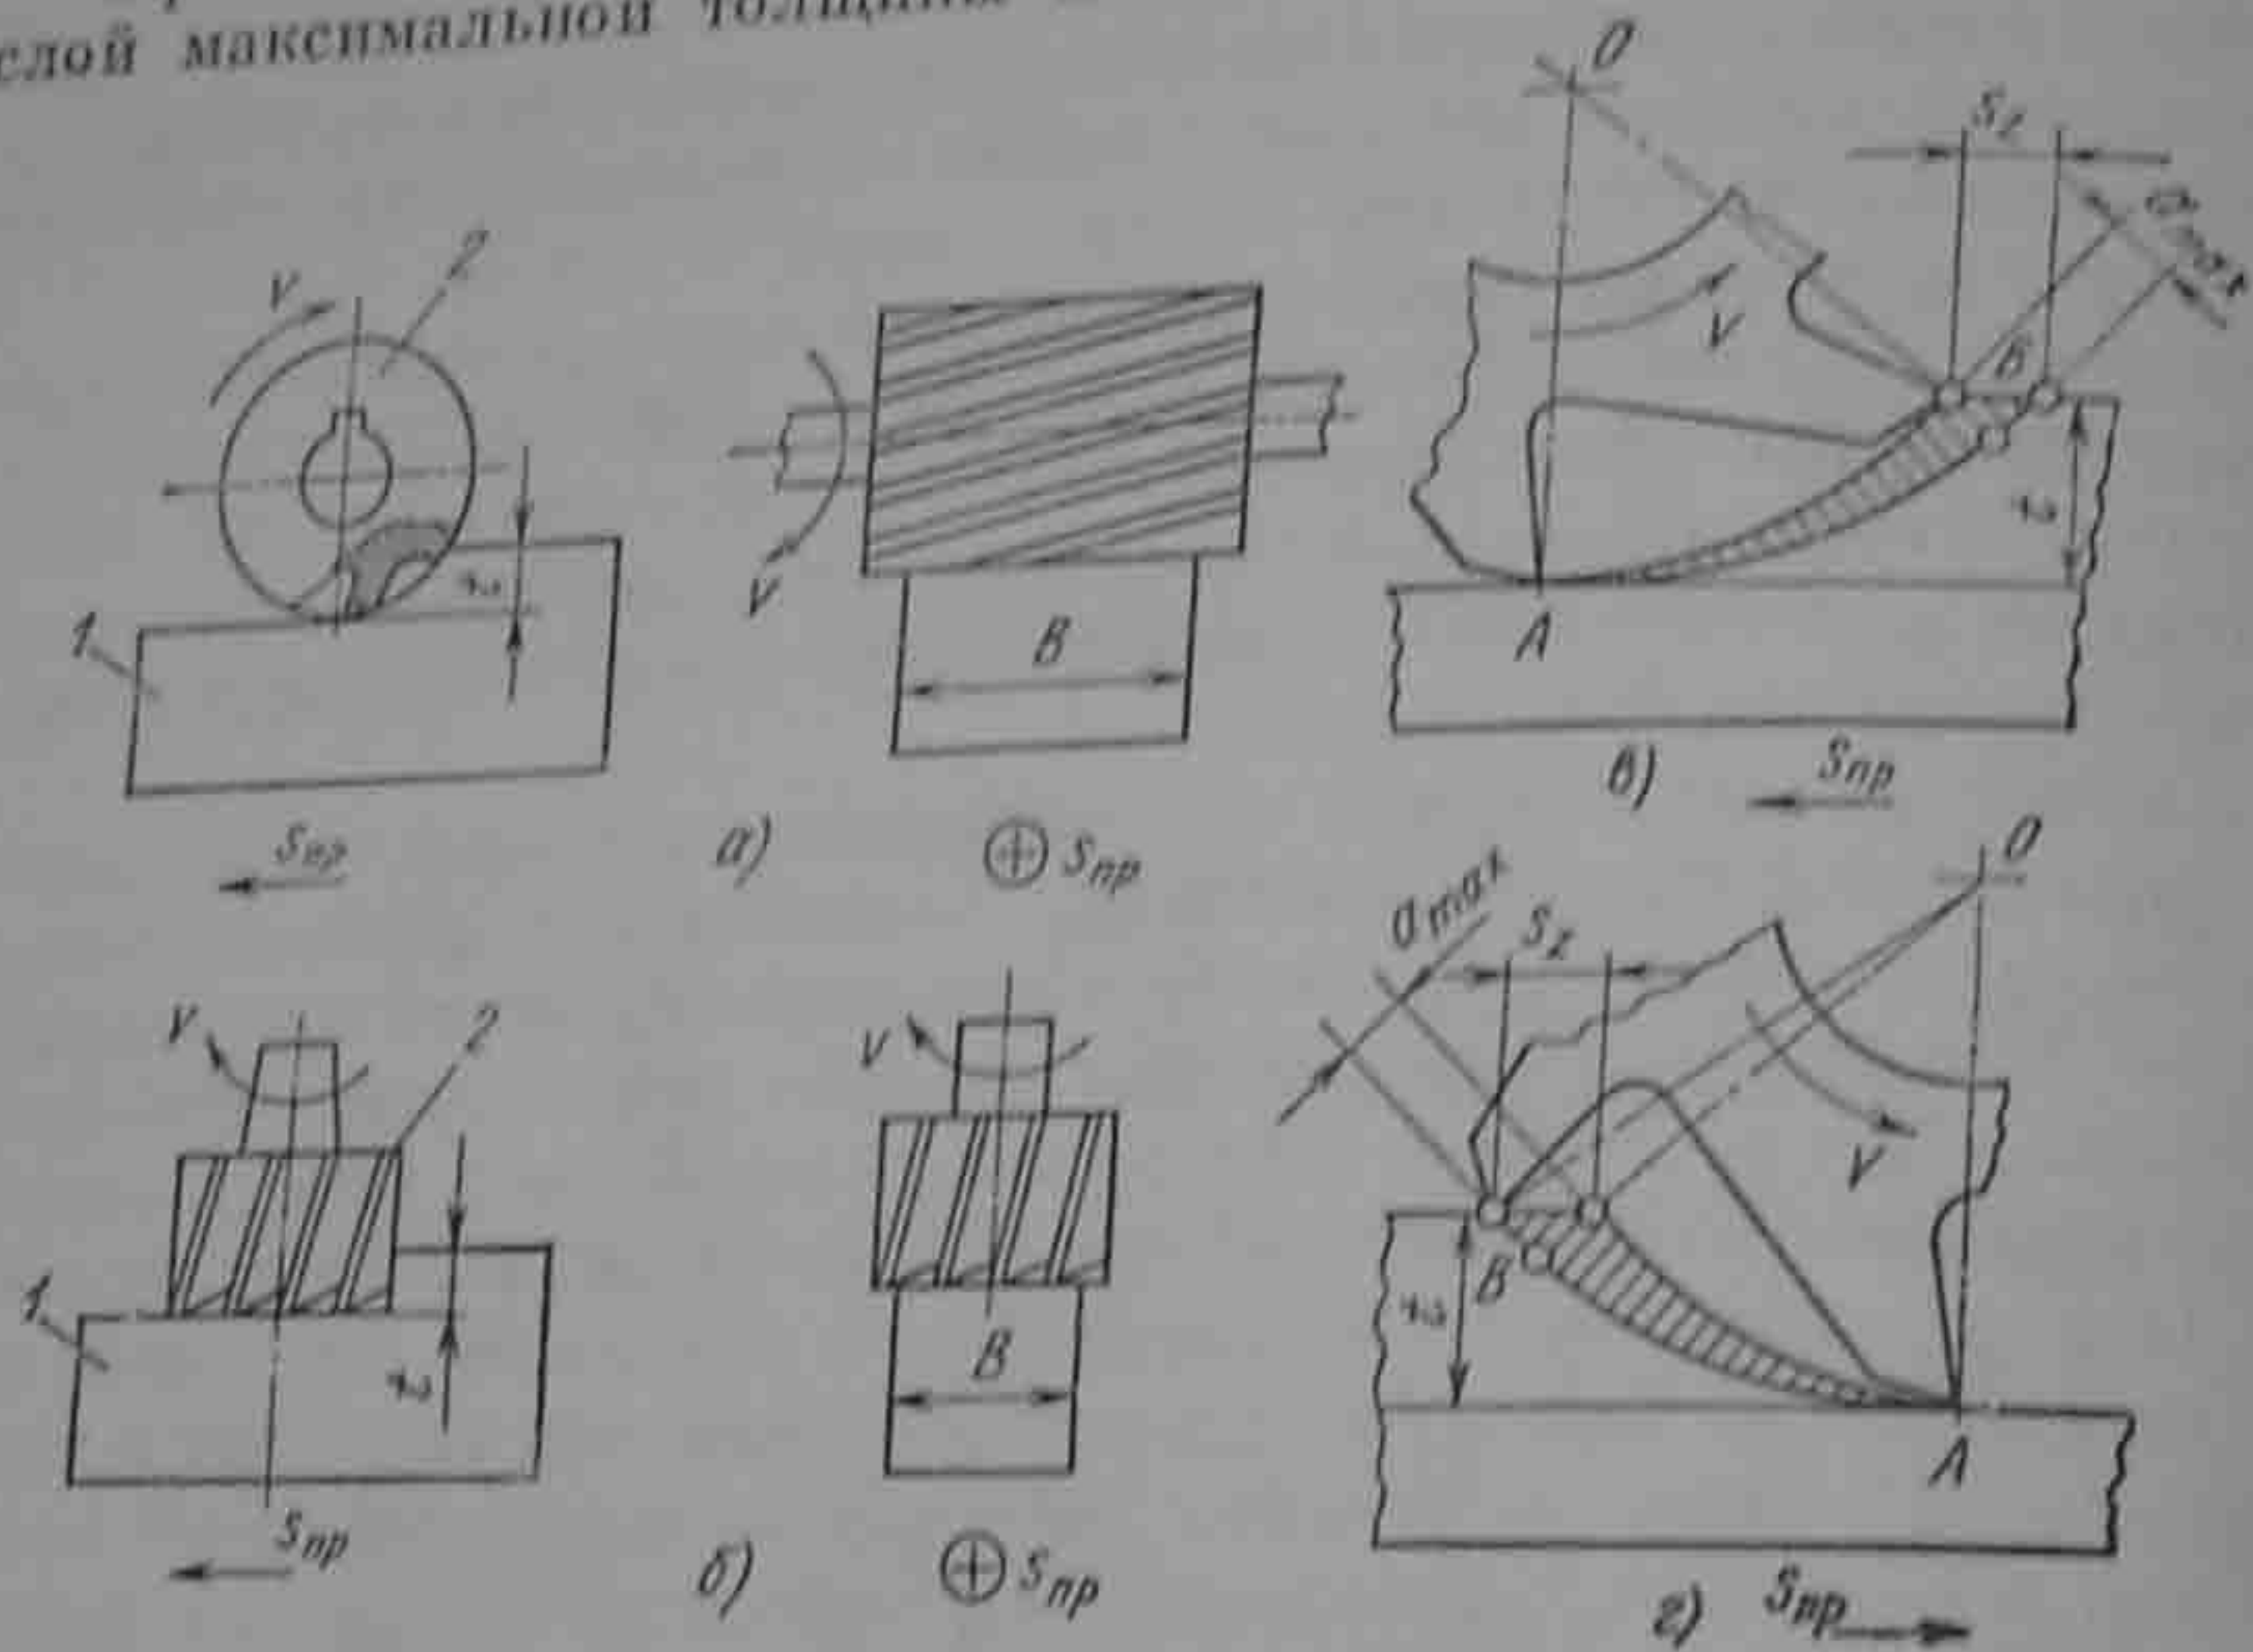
Схемы фрезерования цилиндрической (а) и торцевой (б) фрезой, встречного (а) и попутного (б) фрезерования:
